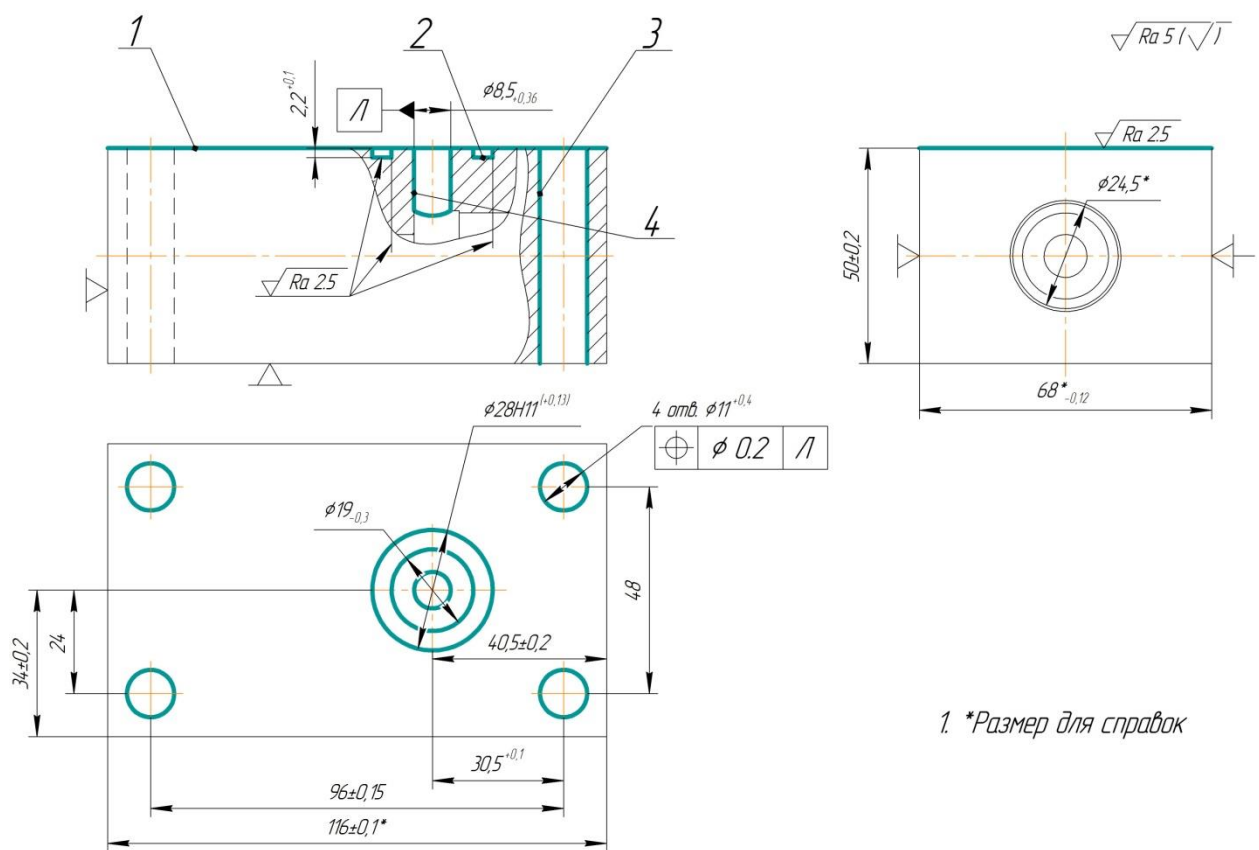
Операционный эскиз фрезерной обработки
